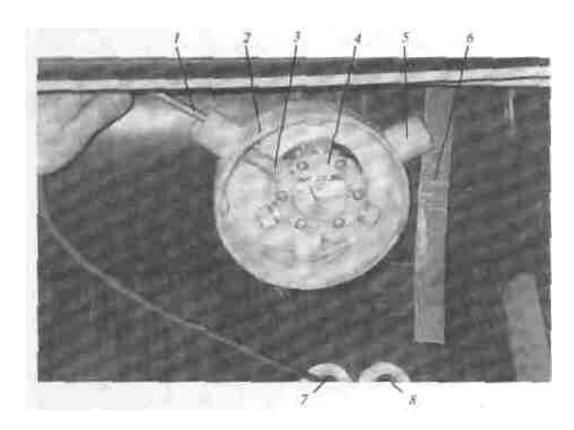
Монтаж арматуры баллона СНГ: 1 – заправочный трубопровод; 2 – вентиляционная коробка; 3 – штуцер; 4 – мультиклапан; 5 – вентиляционный вывод; 6 – хомут; 7 и 8 – вентиляционные штуцеры.
